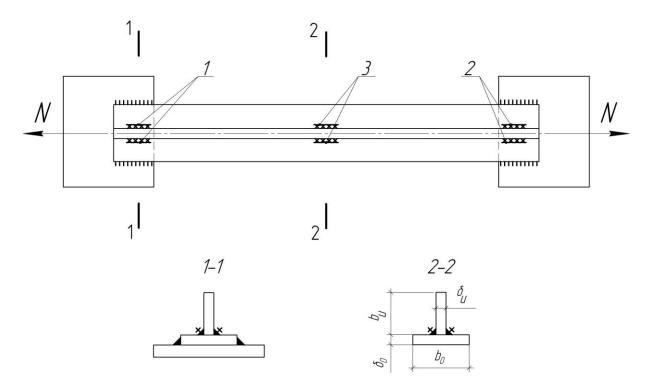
К вопросу о порядке наплавки сварных швов
